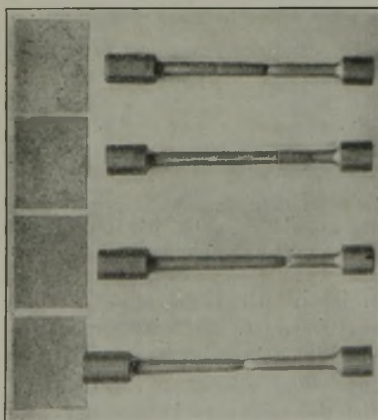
Einfluß der Nachbehandlung der Schweiße auf die Festigkeitseigenschaften. (Gasschmelzschweißung; Flußstahl; Zerreißstäbe nur aus Schweiße bestehend.)
